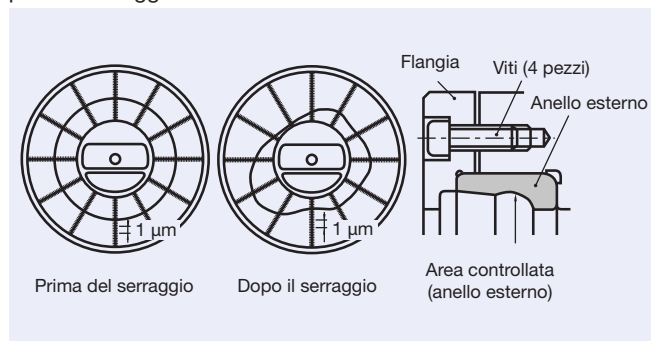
Deformazione della Superficie di Rotolamento per un Serraggio Eccessivo
